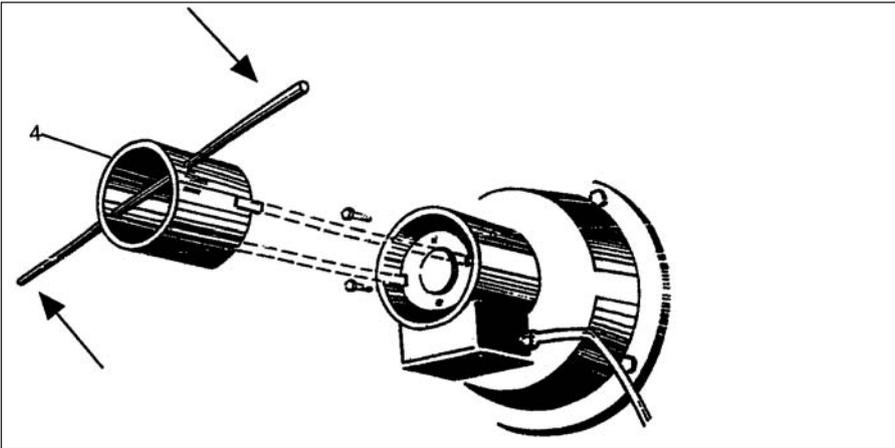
Отпуск аварийного тормоза (захватывающего устройства).
